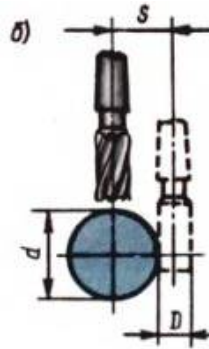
Позиція 12: встановлення фрези у діаметральній площині вала
